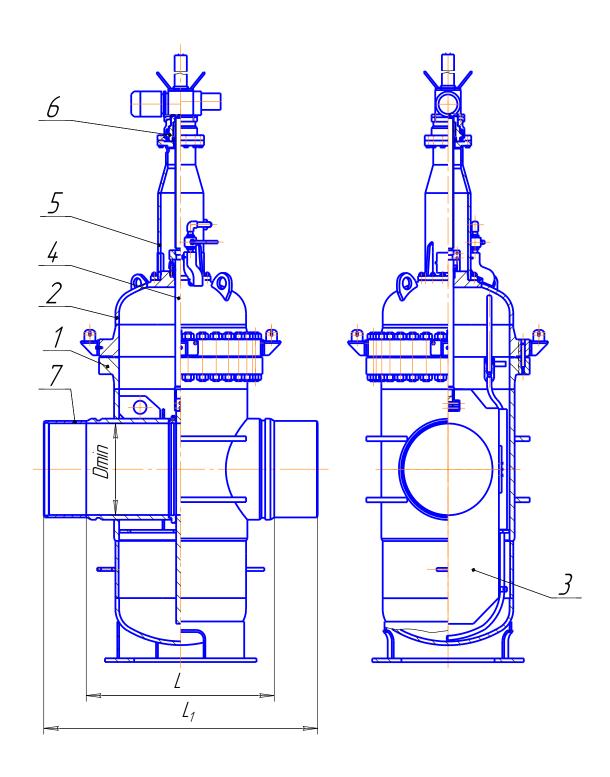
Штампосварная задвижка под приварку к трубопроводу
